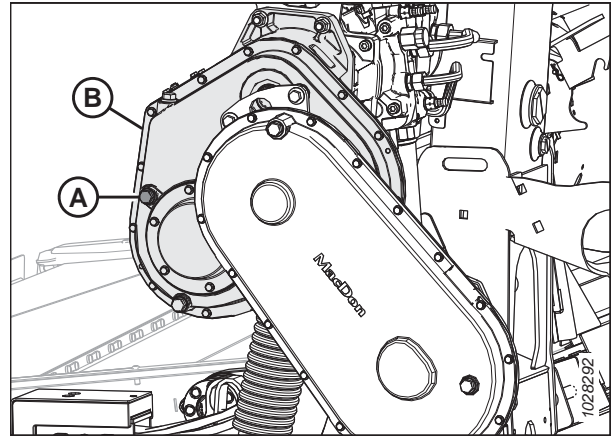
Schneidwerk-Hauptgetriebe
